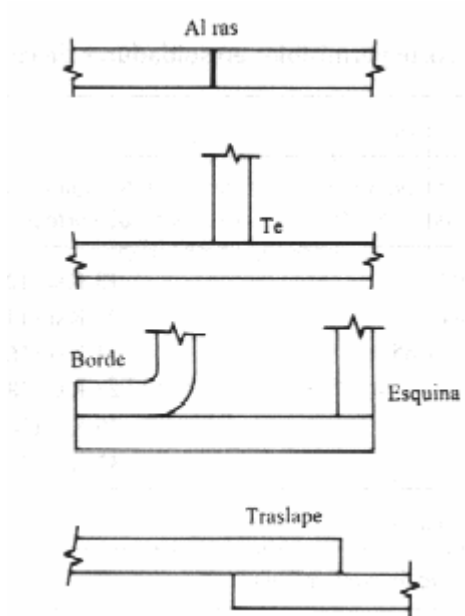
Tipos de ensamblajes soldados.
